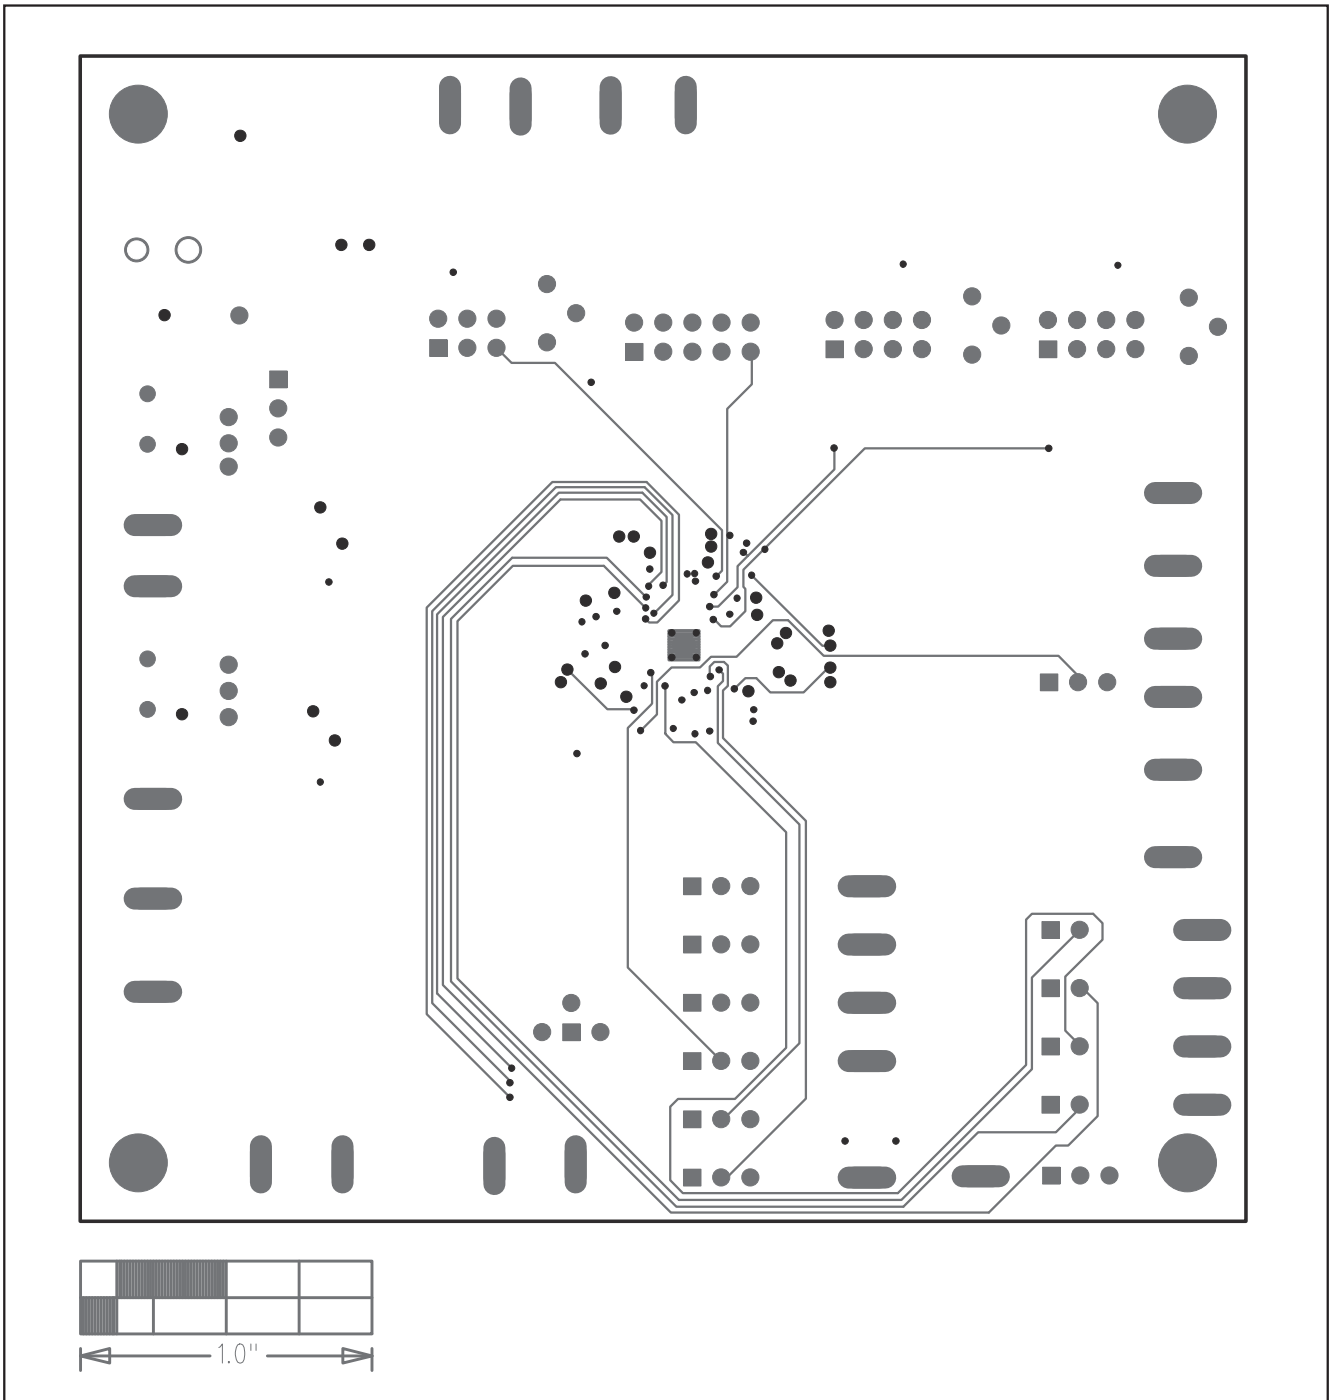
MAX8671评估板PCB布局—焊接层, 第6层
